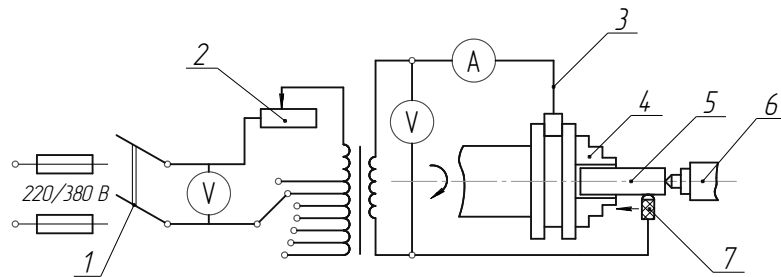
Принципова схема електромеханічної обробки на токарному верстаті: 1 – вмикач; 2 – регулятор; 3 – підведення струму; 4 – патрон; 5 – заготовка; 6 – задній центр; 7 – інструмент
